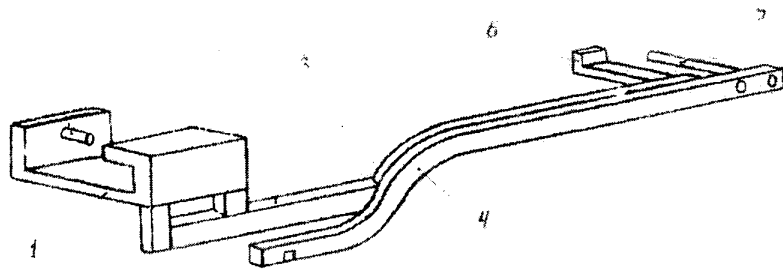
Приспособление ПНВ-4 для навески верхняков IR20B:
